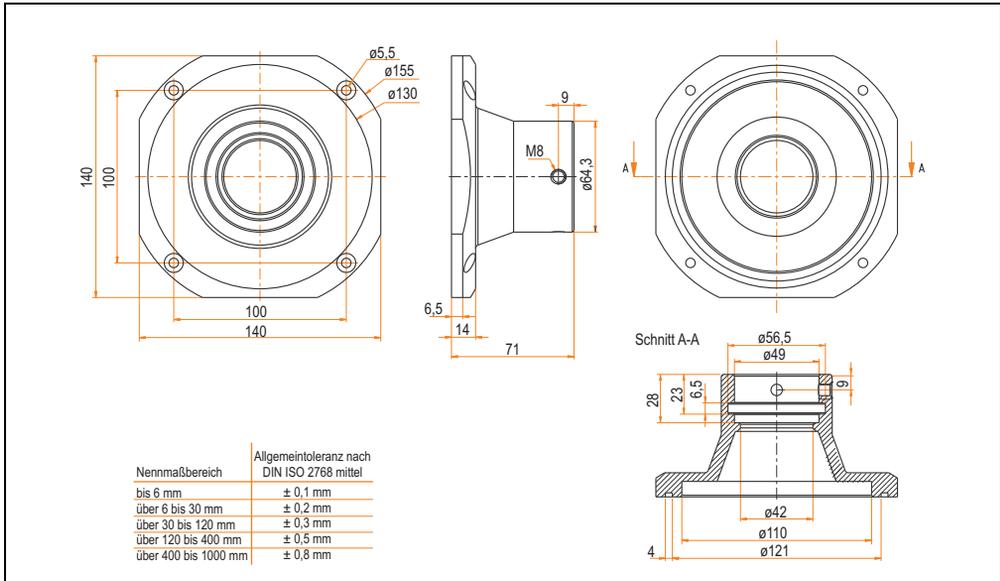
Abmessungen Extension Flansch 5AC800.FLG1-00
